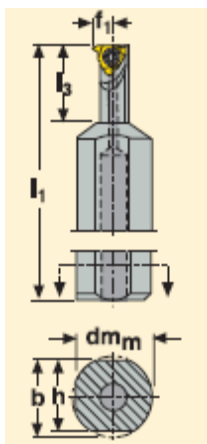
Державка токарная внутренняя SHR 0020L09A
